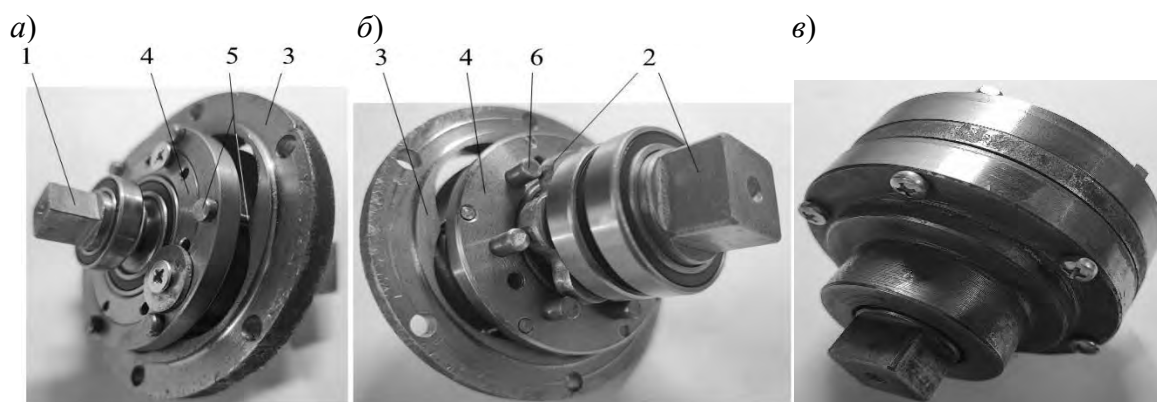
Первая ступень (а), вторая ступень (б) и циклоидально-цевочный редуктор *Cyclo-80-36* в сборе (в): 1 – ведущий вал; 2 – ведомый вал с центральным циклоидальным колесом; 3 – неподвижное циклоидальное колесо; 4 – двухвенцовый сателлит; 5, 6 – ролики (цевки) двух венцов сателлита
